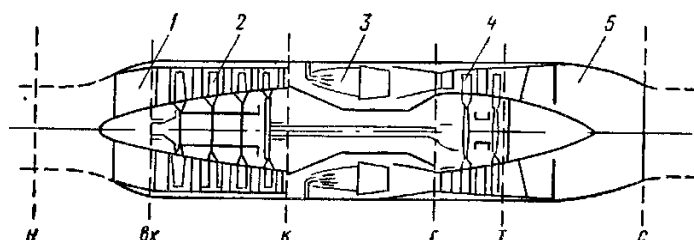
Турбореактивний двигун: 1 – вхідний пристрій; 2 – компресор; 3 – камера згоряння; 4 – турбіна; 5 – вихідний пристрій
